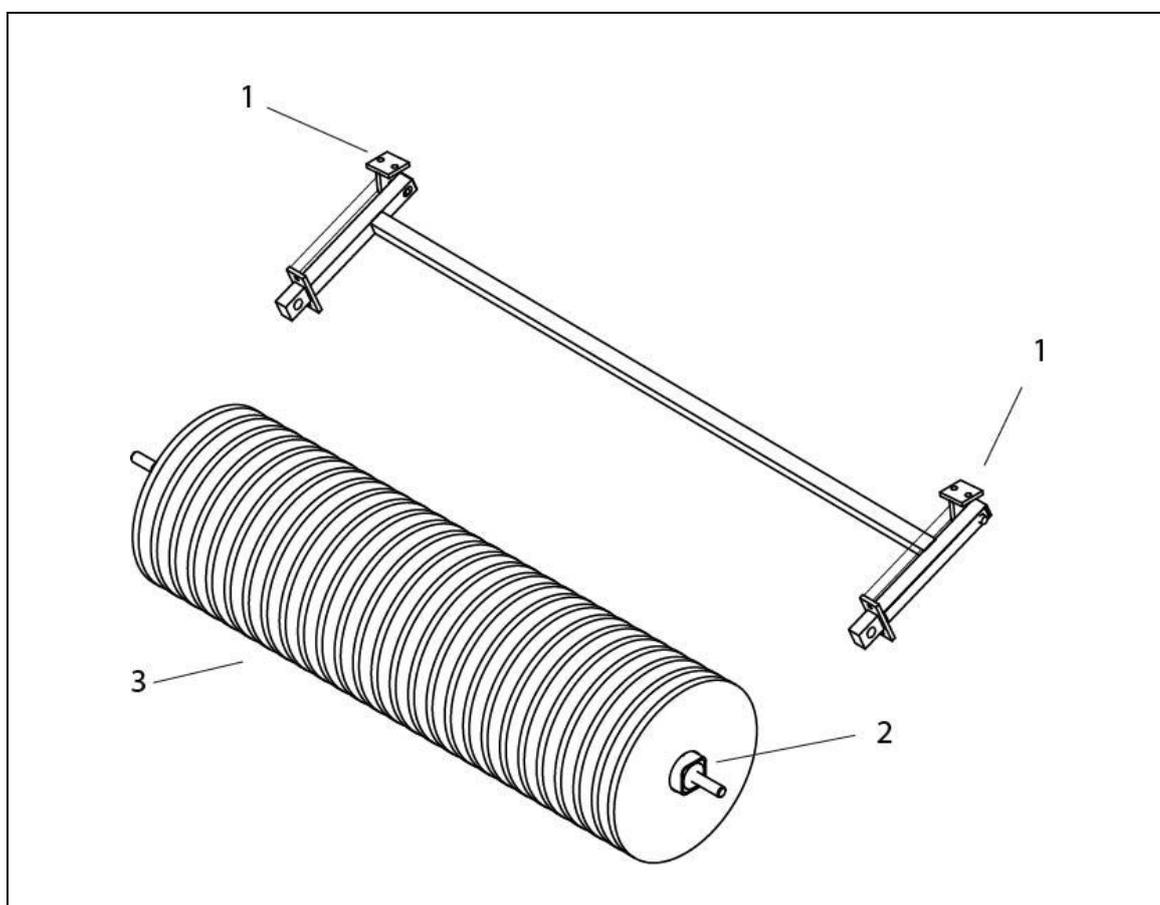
Struttura e fissaggio degli elementi della spazzola
